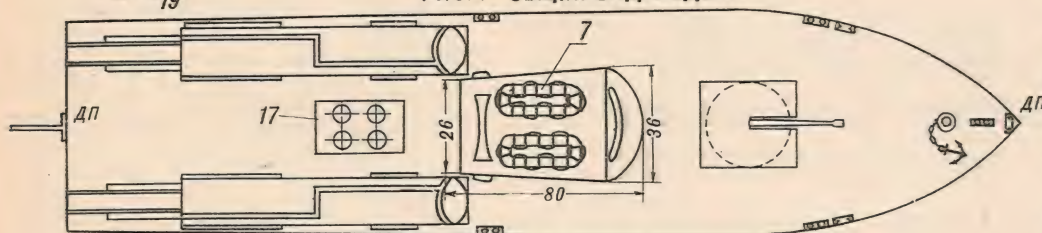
КОНТУРЫ БОКА И ПАЛУБЫ КОРПУСА
